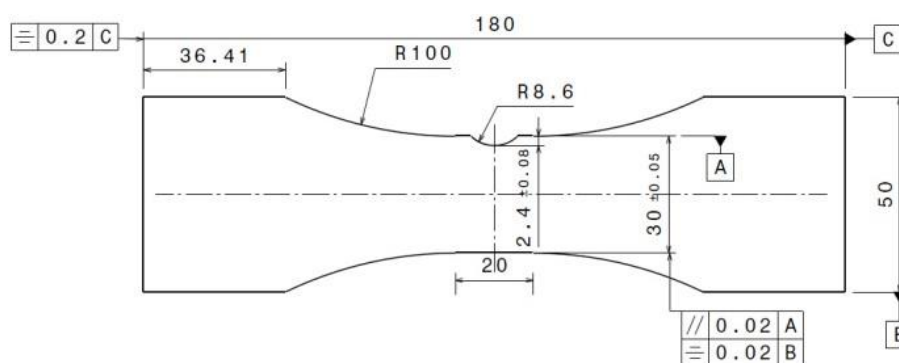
Géométrie de l'éprouvette de fatigue entaillée  $K_t=2$
